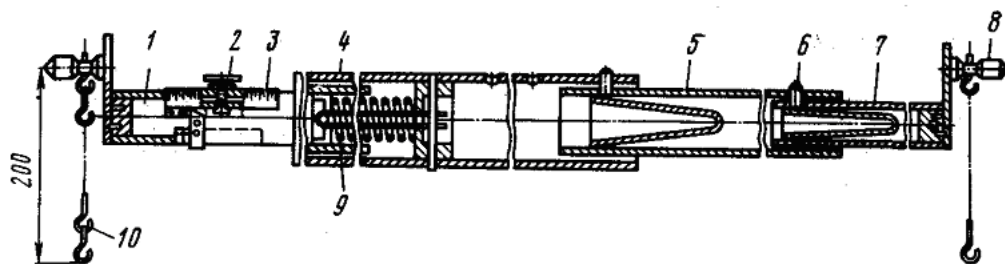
Телескопическая линейка для замера схождения колес: 1 – подвижная труба; 2 – винт; 3 – шкала; 4 – неподвижная труба; 5 – промежуточная труба; 6 – фиксатор; 7 – удлинитель; 8 – контактный наконечник; 9 – пружина; 10 – цепочка
